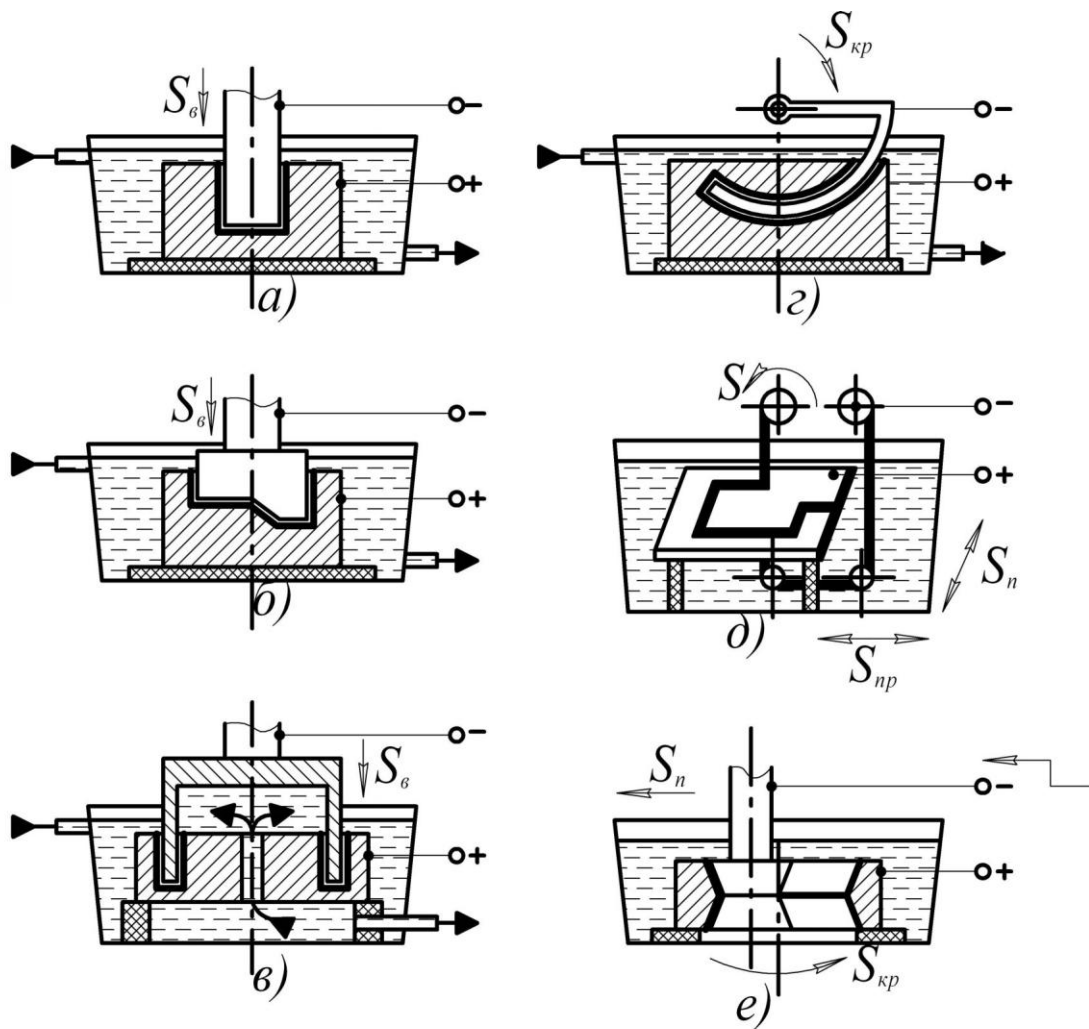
Схеми електроіскрової обробки *а* - прошивання отвору; *б* - обробка фасонної порожнини штампа; *в* - прошивання отвору за способом трепанації; *г* - прошивання криволінійного отвору; *д* - вирізування заготовки з листа; *е* - шліфування внутрішньої поверхні фільери
